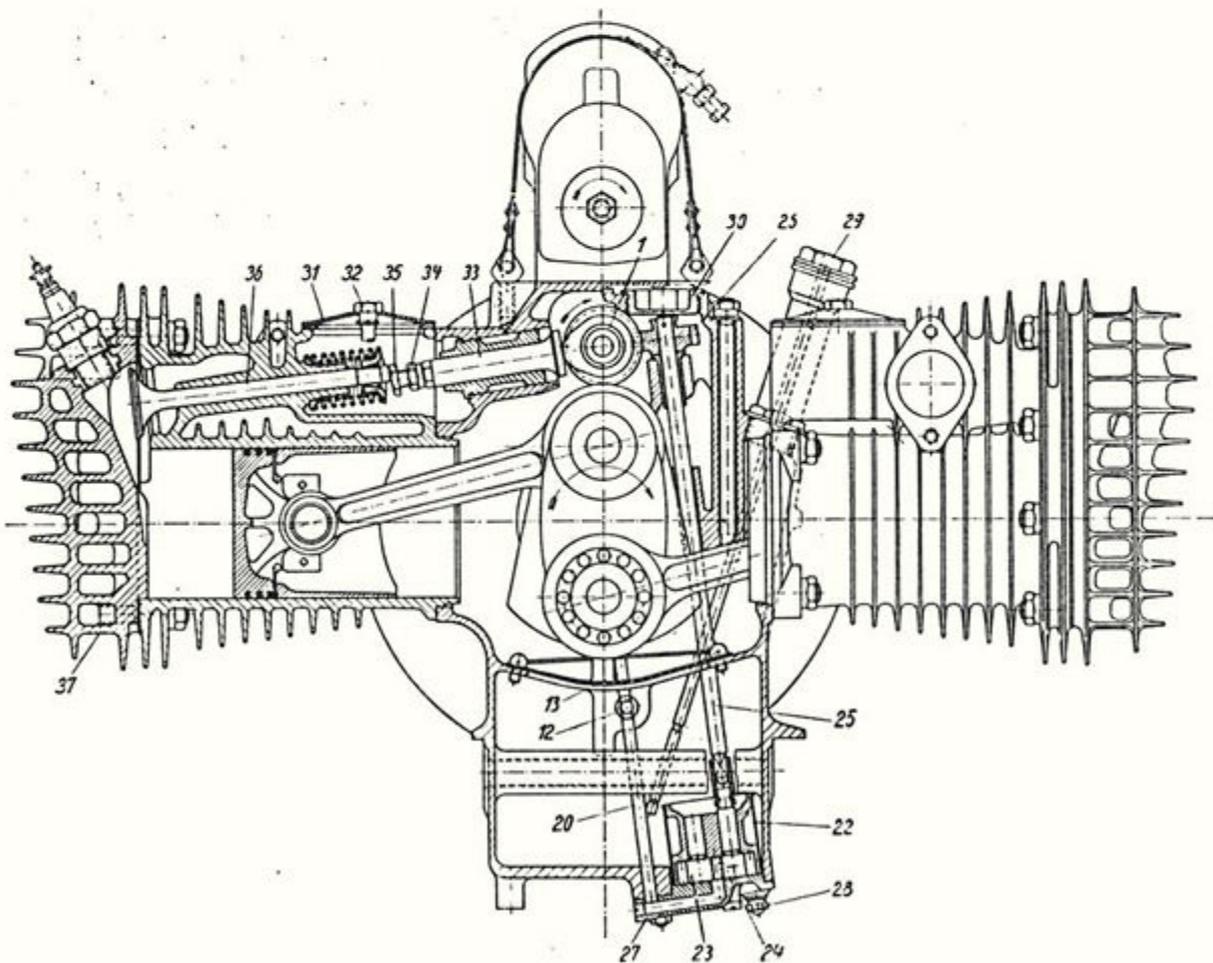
Tourenmotor mit teilweiseem Querschnitt durch die Zylindermittle
